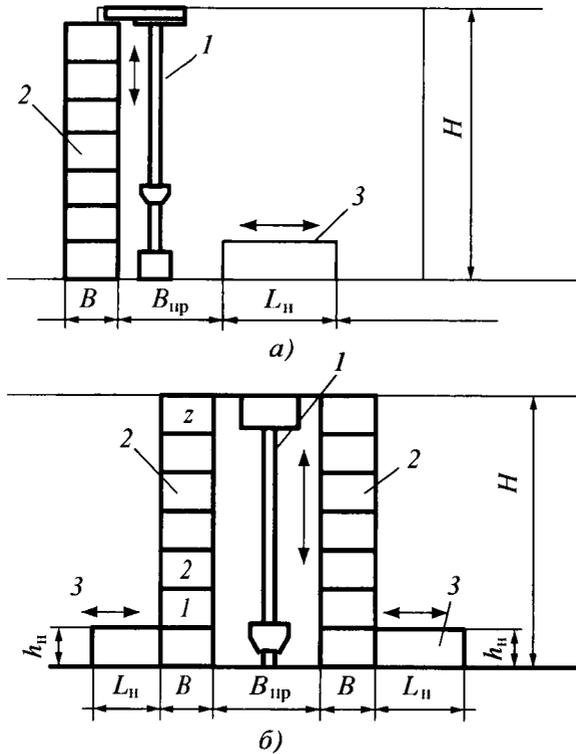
Типовые схемы поперечного сечения складов ГАП с автоматическим стеллажным краном-штабелером 1, одним (а) и двумя (б) стеллажами 2 и накопителями 3:
